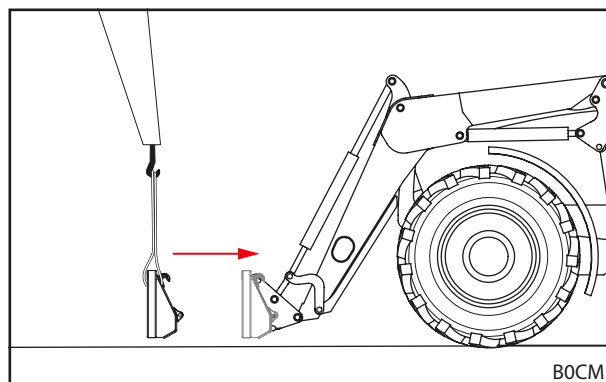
Accrocher le cadre dans le cadre porte-outils
